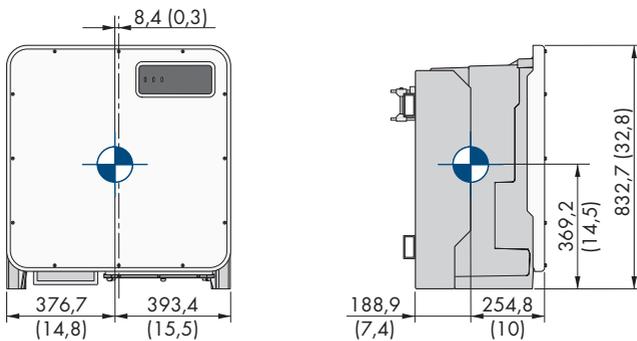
Dimensionado del centro de gravedad del producto (medidas en mm [in])
